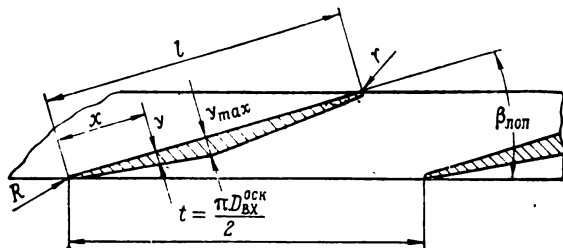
Развертка цилиндрического сечения по диаметру лопастей осевого предвключенного колеса.
